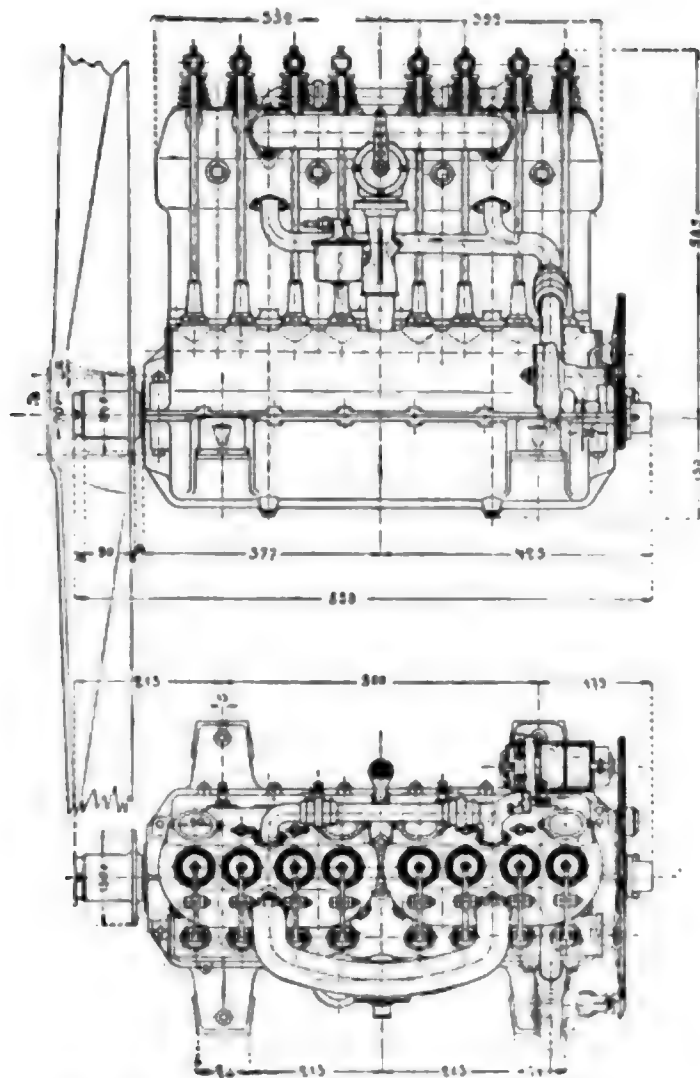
u. Fig. 276. Seitenansicht und Draufsicht.
